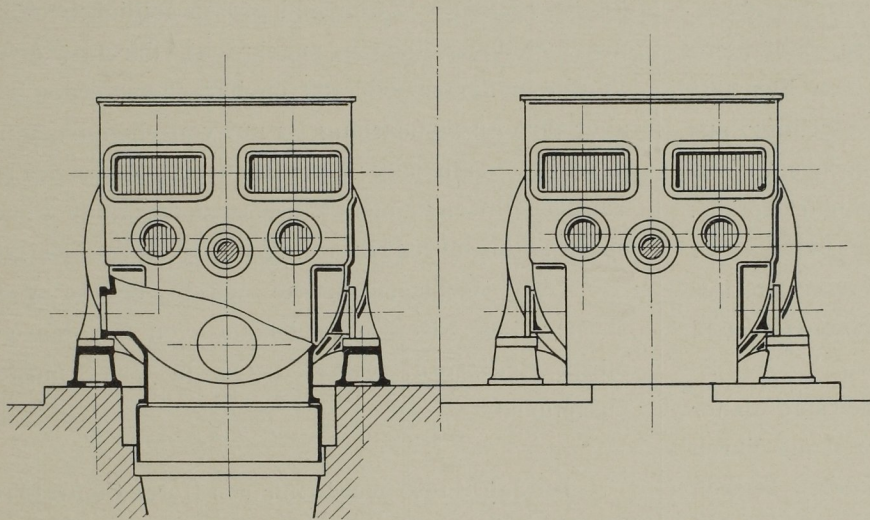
Stirnansicht der Gebläsecylinder. Massst. 1:60.
